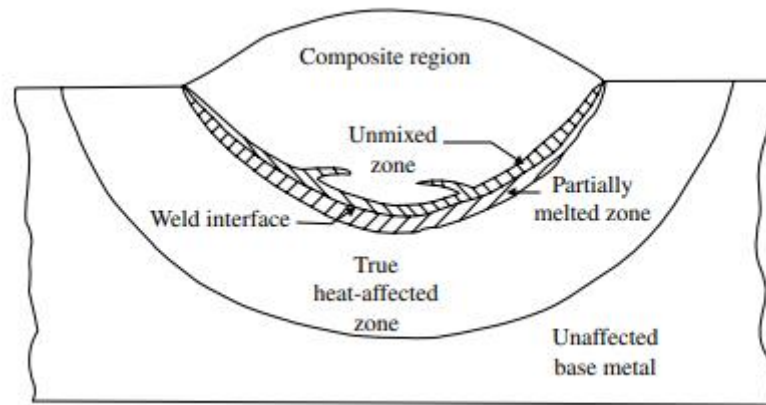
Régions d'une soudure par fusion (Ref. [27]. © AWS)
